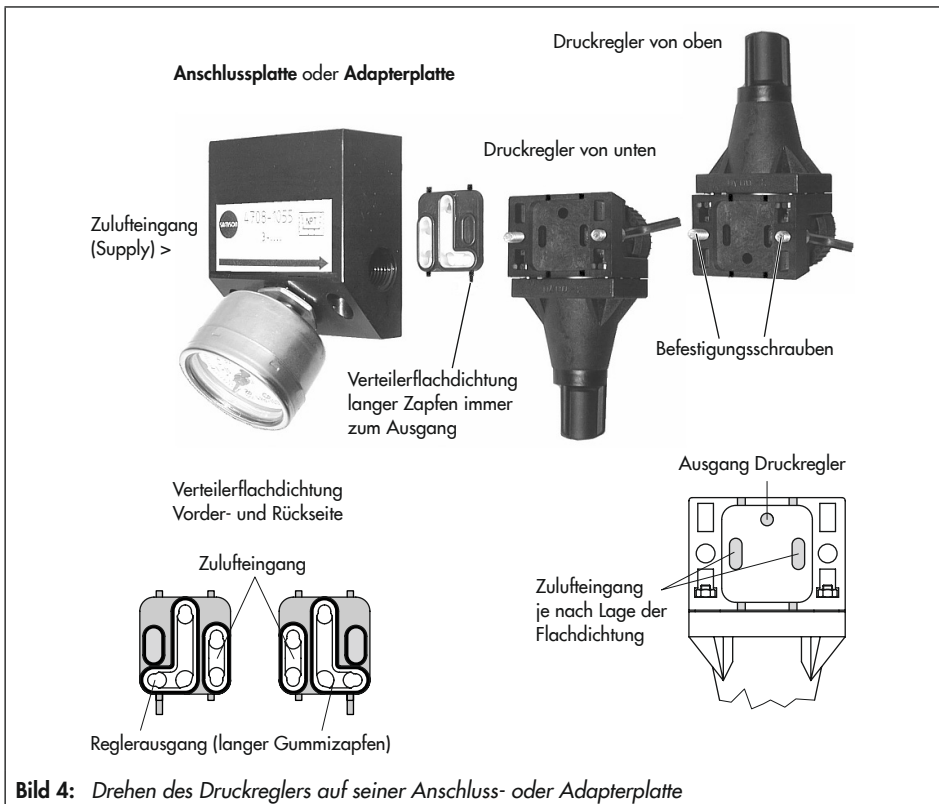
Drehen des Druckreglers auf seiner Anschluss- oder Adapterplatte
